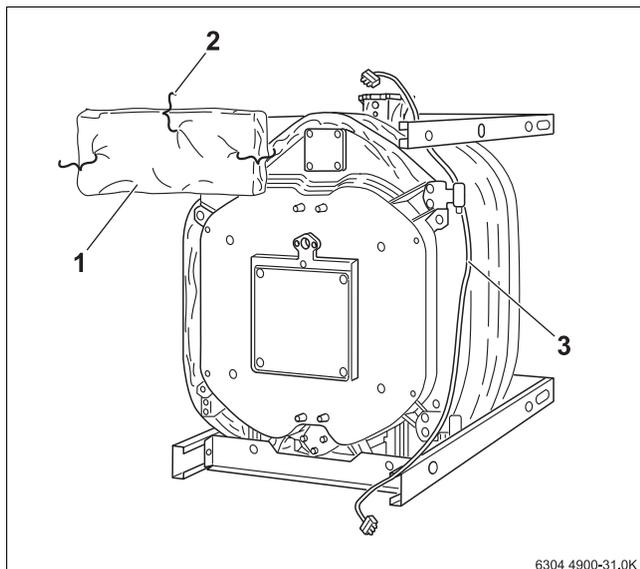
Rechteckiger Wärmeschutz und Brennerkabel montieren
